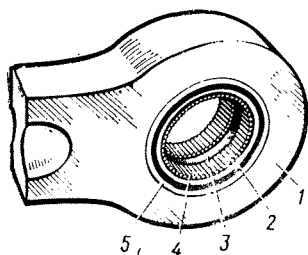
Головка поршневого дышла с иглольчатым подшипником
